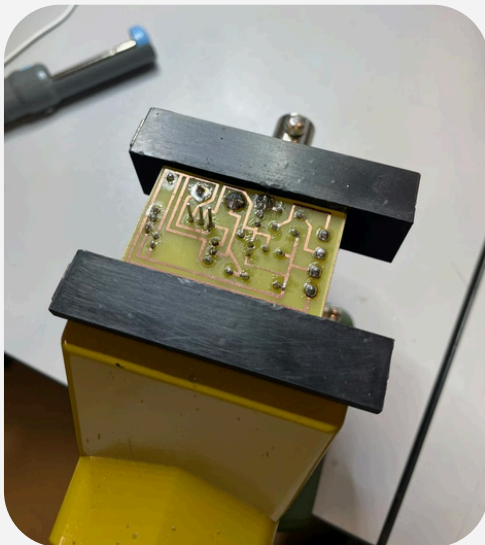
SOUDAGE DU CIRCUIT IMPRIMÉ
